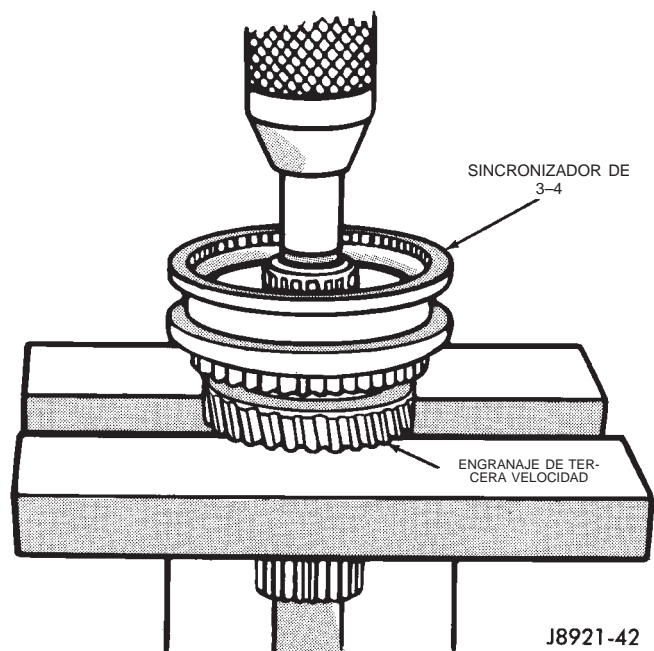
Desmontaje de sincronizador de 3-4 y engranaje de tercera velocidad
